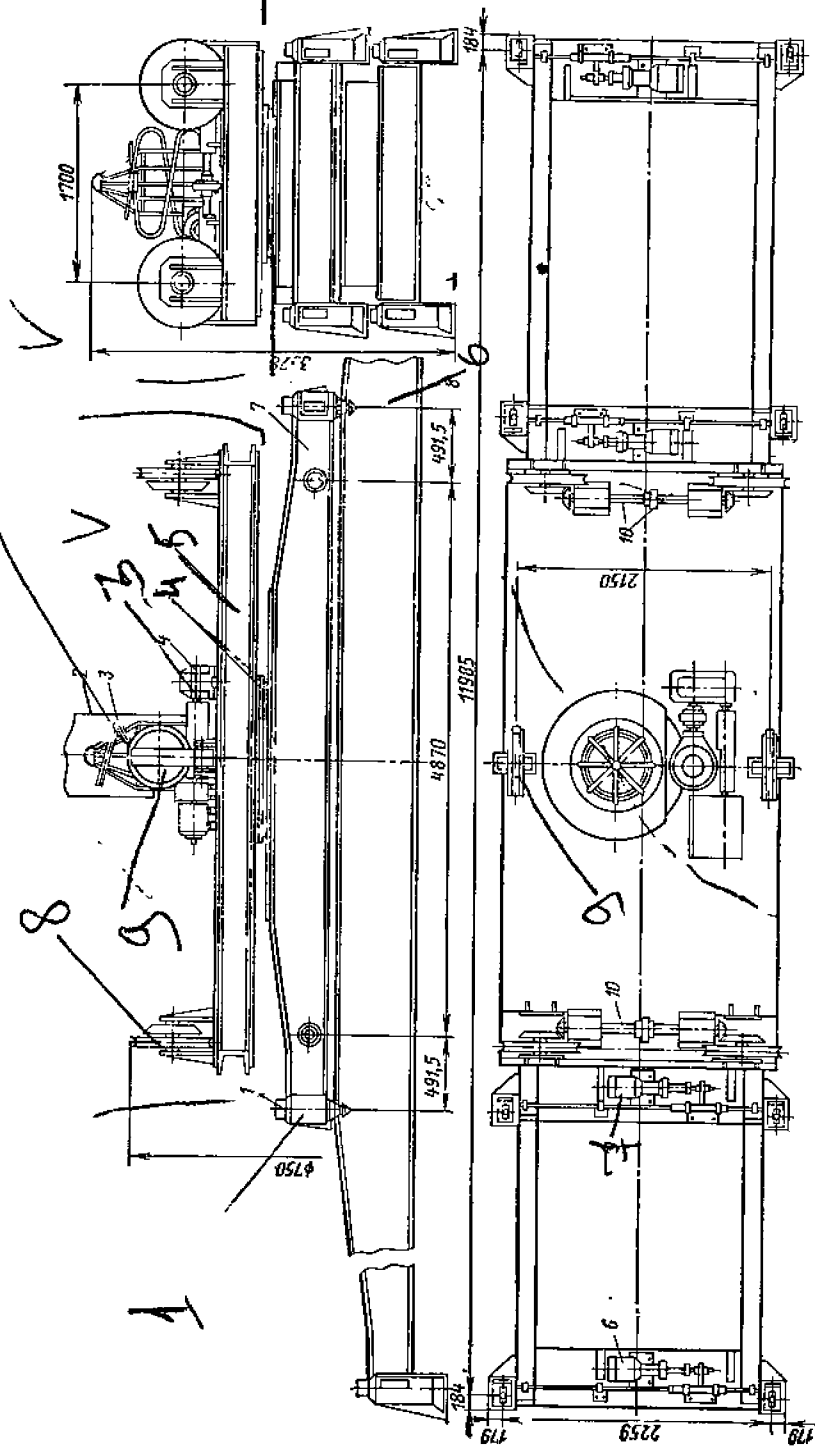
Контейнерное ГУ с управляемым поворотным штырем: 1 — поворотные штыри; 2 — кожух; 3 — корзина для укладки электрокабеля; 4 — механизм вращения; 5 — опорно-поворотное устройство; 6 — блочная рама; 7 — грузозахватная рама для контейнеров типа 1С; 8 — грузозахватная рама для контейнеров типа 1А; 9 — механизм поворота штырей; 10 — механизм балансировки канатных блоков
